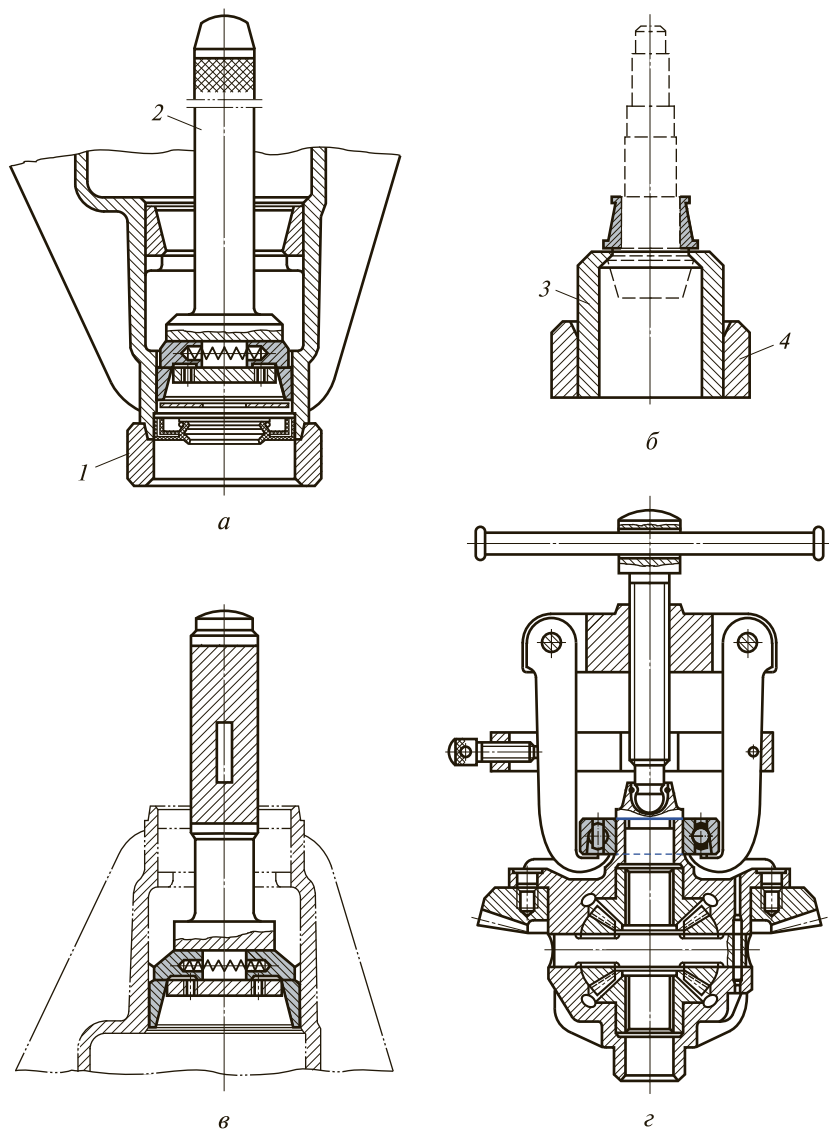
Приспособления для разборки редуктора заднего моста автомобилей «Москвич-412», «Москвич-2140»:
